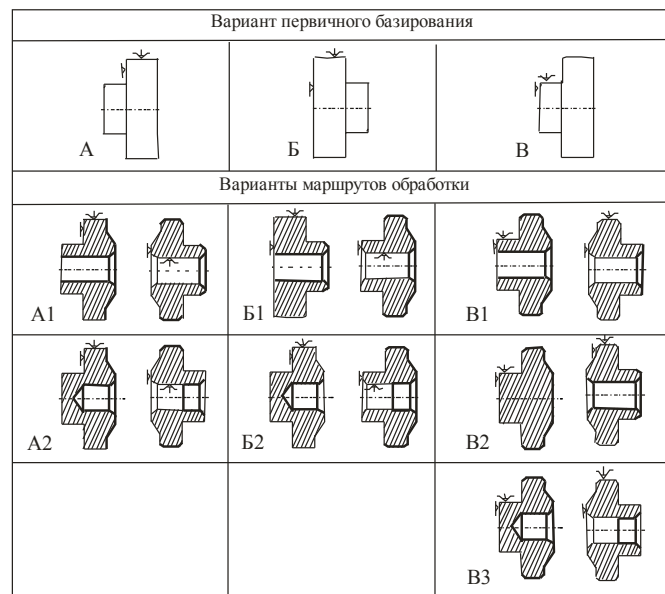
Варианты первичного базирования заготовки и маршрутов обработки
